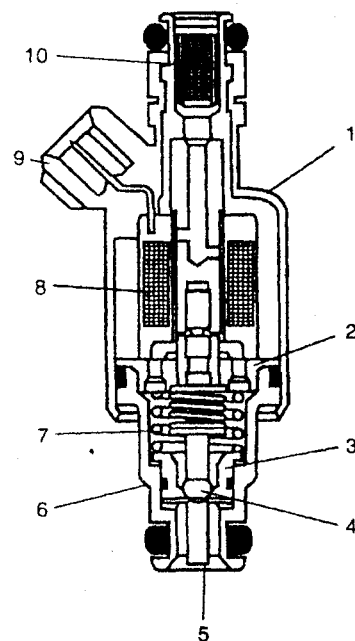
Топливная форсунка: 1 – корпус форсунки; 2 – направляющая пластинка с проставкой; 3 – седло клапана; 4 – шариковый клапан; 5 – распылительная насадка; 6 – корпус распылителя; 7 – сердечник с пружиной; 8 – катушка; 9 – разъем; 10 – сетчатый фильтр
